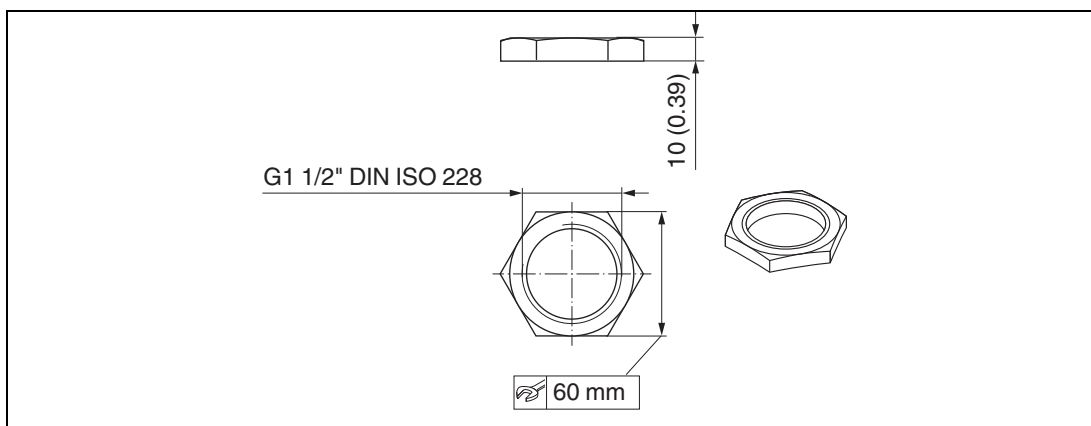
Abmessungen Befestigungsmutter, Maßeinheit: mm (Zoll)
